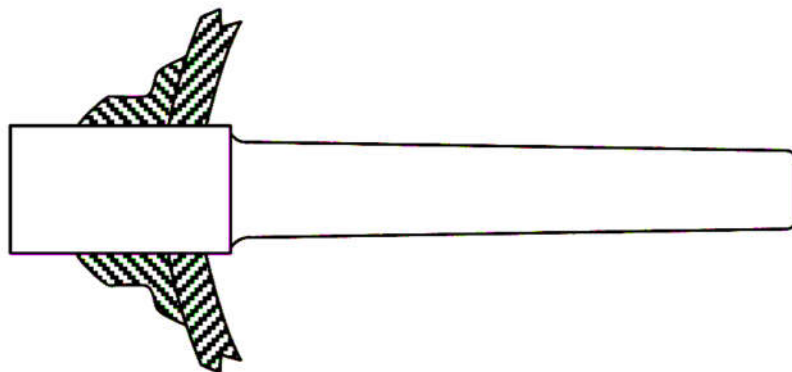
Пример установки гильзы под приварку через адаптер (Socket Weld).
